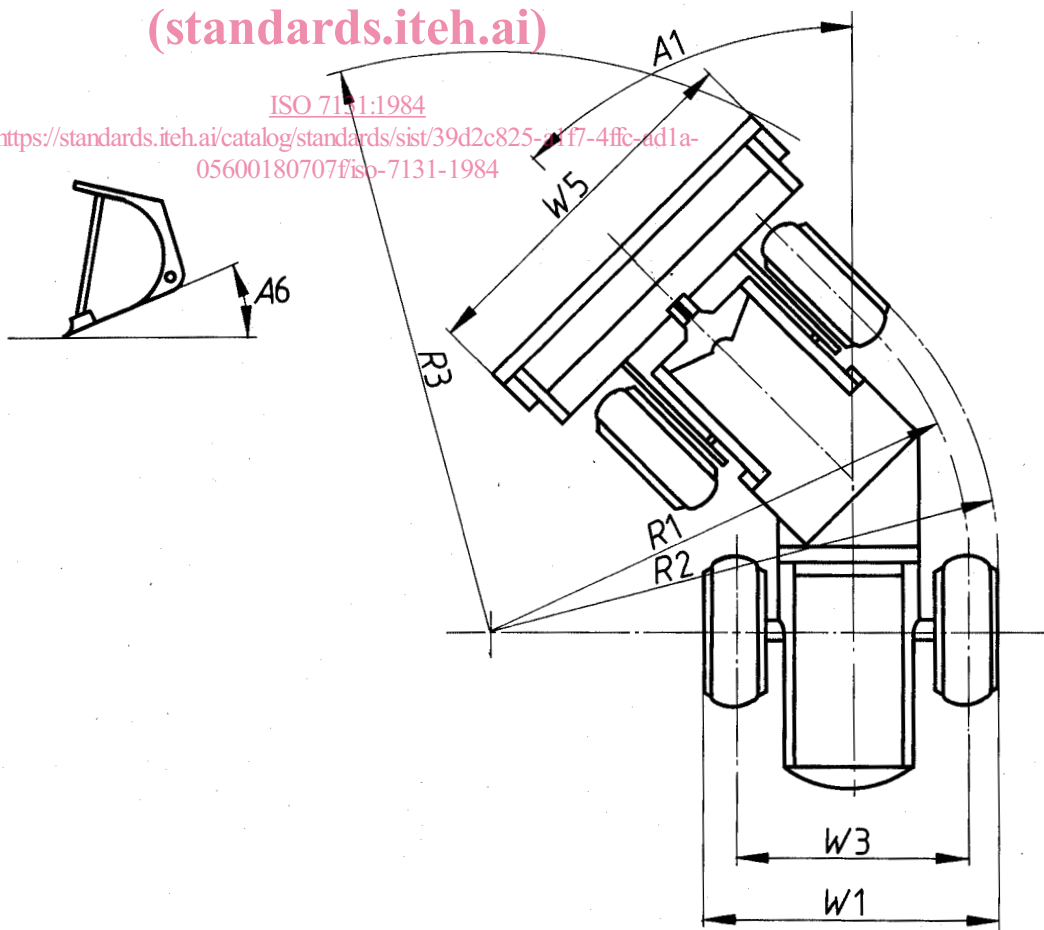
Dimensions de l'engin de base (chargeuse à roues)
